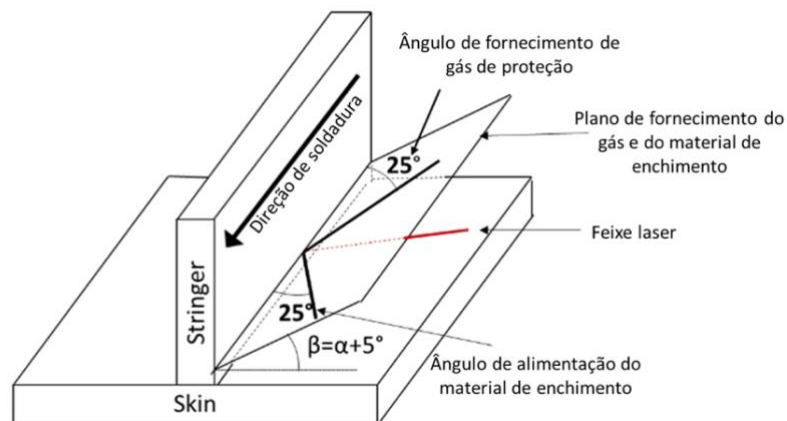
Representação da junta T e dos ângulos utilizados na soldadura
